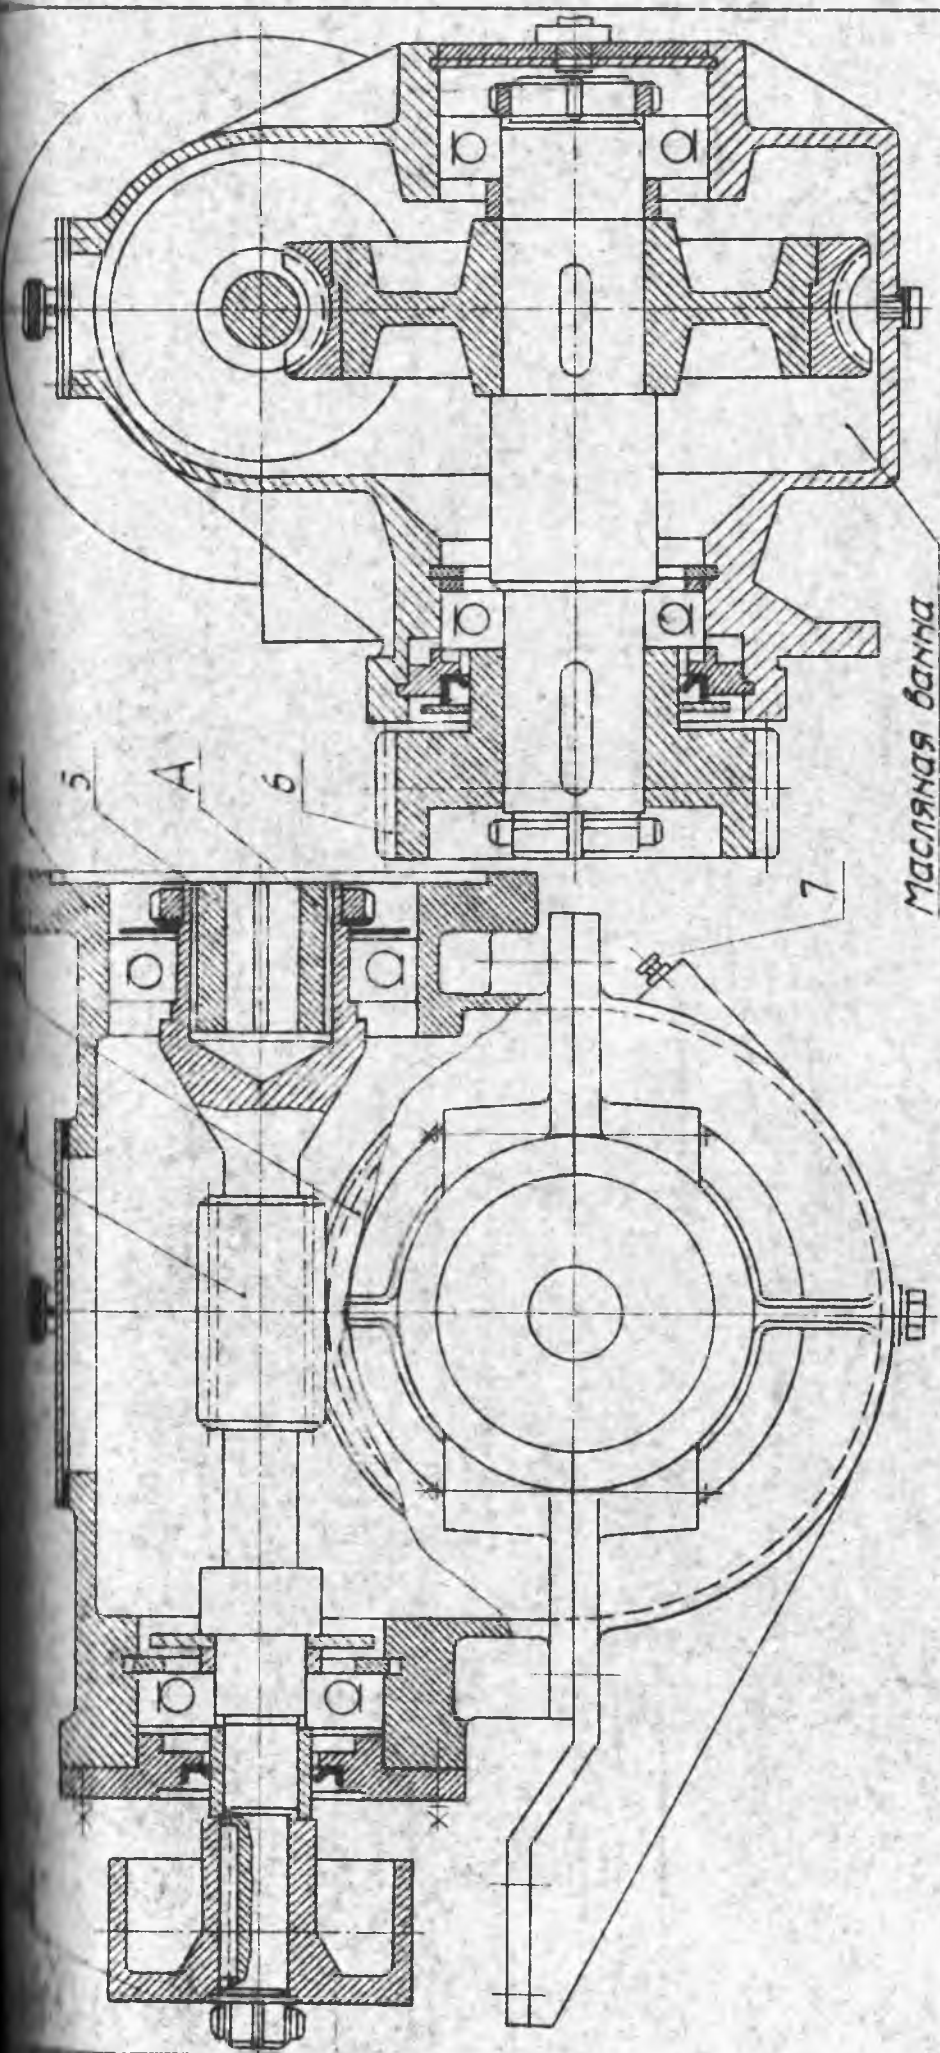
Редуктор червячный А-210 механизма передвижения.
